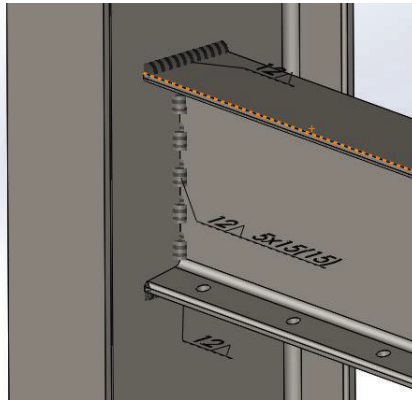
Cordón soldadura perfil ipn guillotina plegadora.
